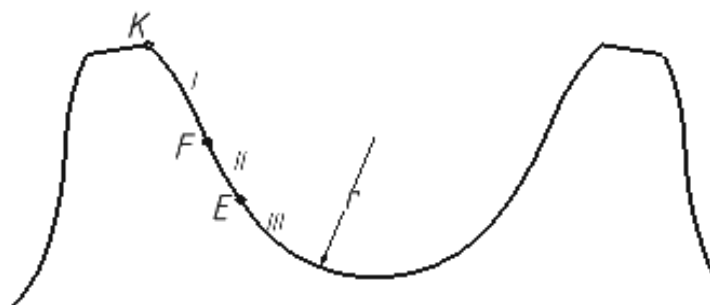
Схема профиля зуба звездочки цепной втулочно-роликовой передачи:
